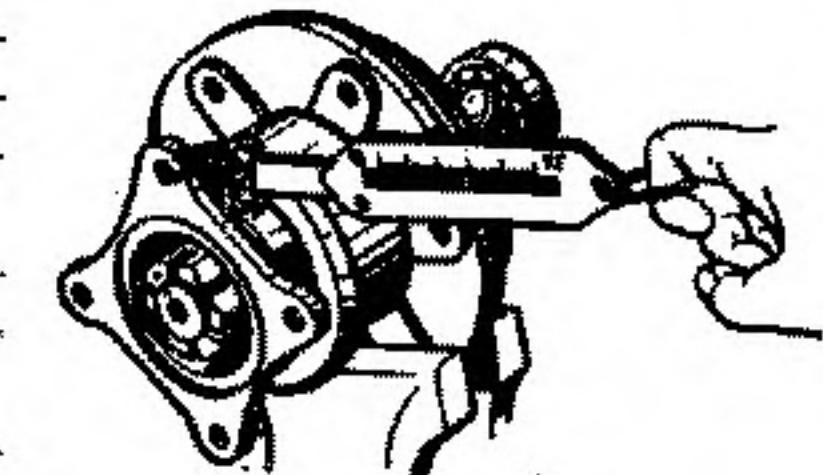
Проверка затяжки подшипников ведущей шестерни
